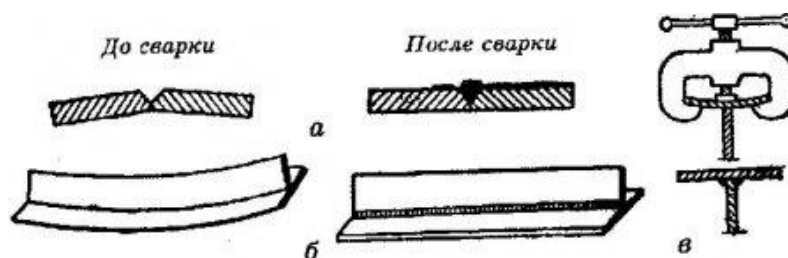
Обратные деформации и положения элементов изделия после сварки: а - стыковое соединение двух пластин; б - тавровая балка; в - полка таврового соединения
